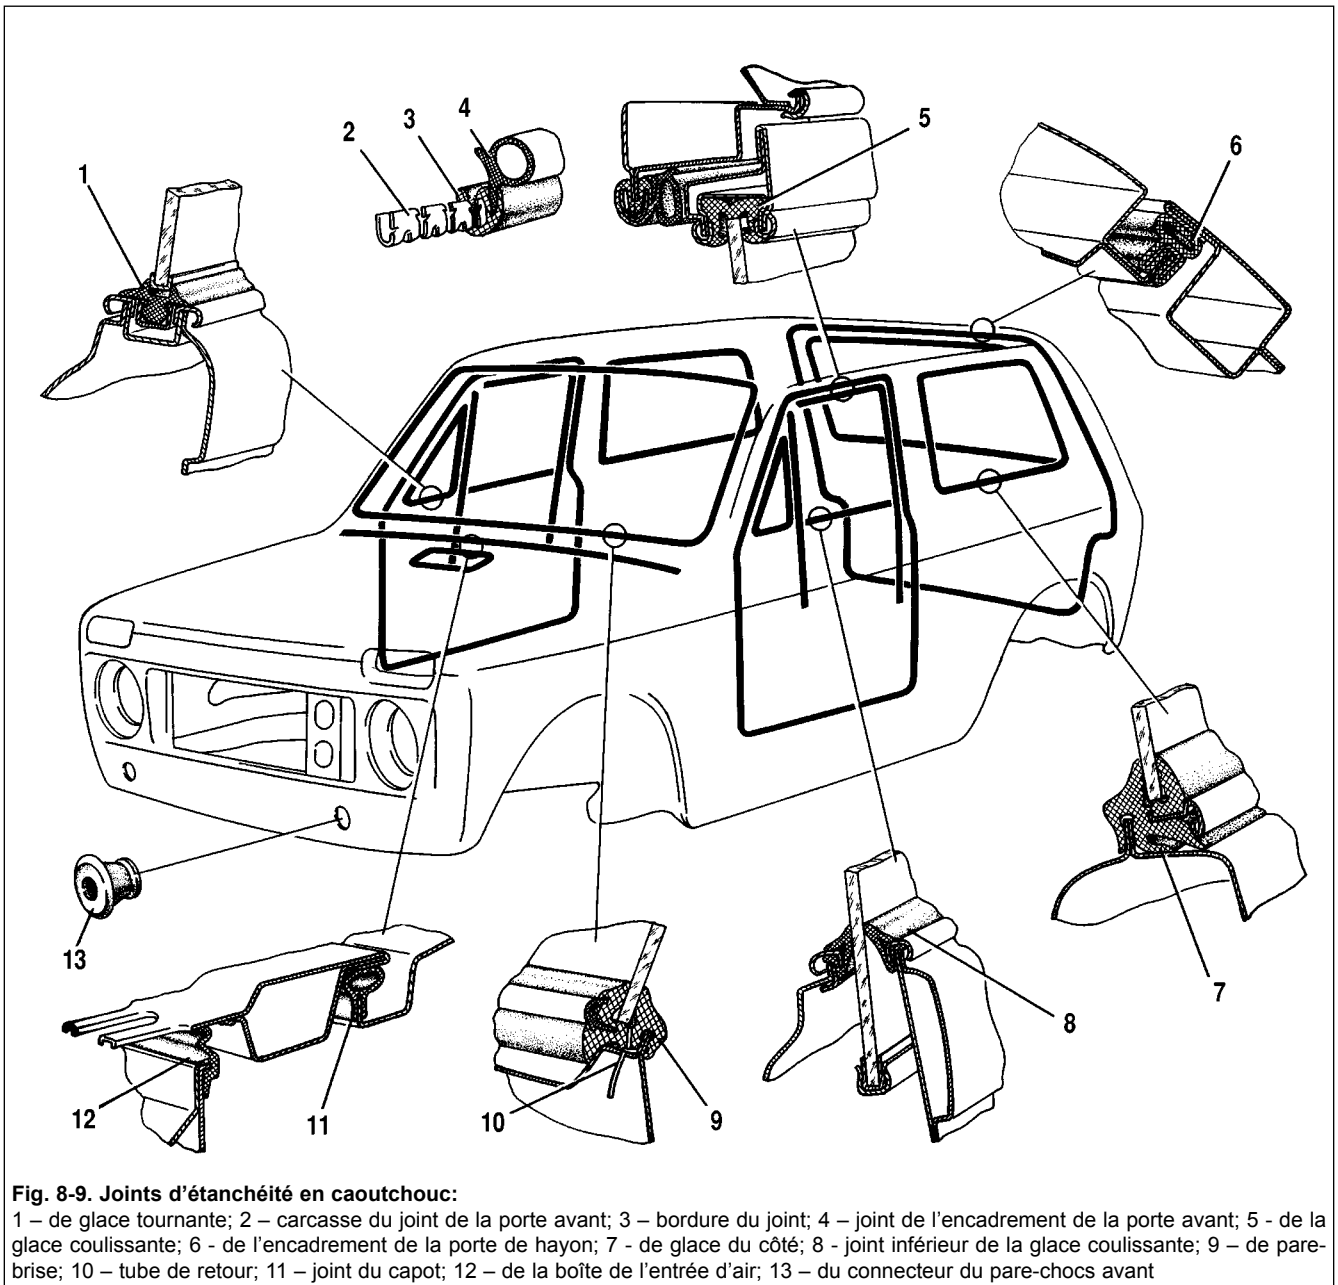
Joints d'étanchéité en caoutchouc:
